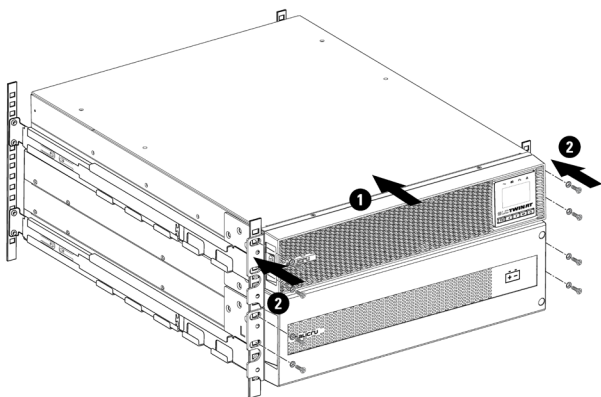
Instalación del SAI y módulo de baterías en el armario rack.
